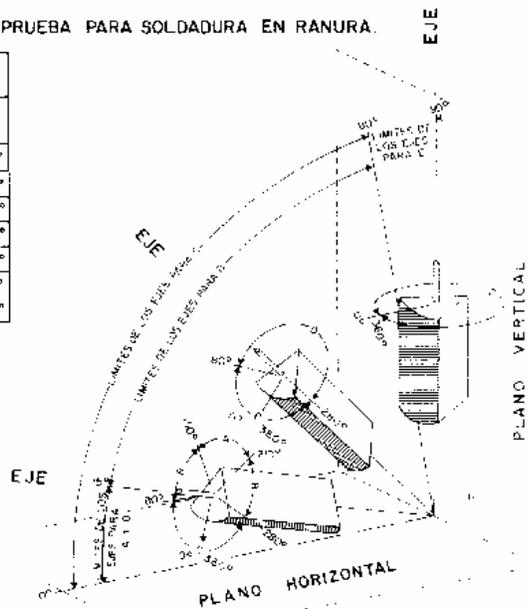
POSICIONES DE LAS PLACAS DE PRUEBA PARA SOLDADURA EN RANURA.
